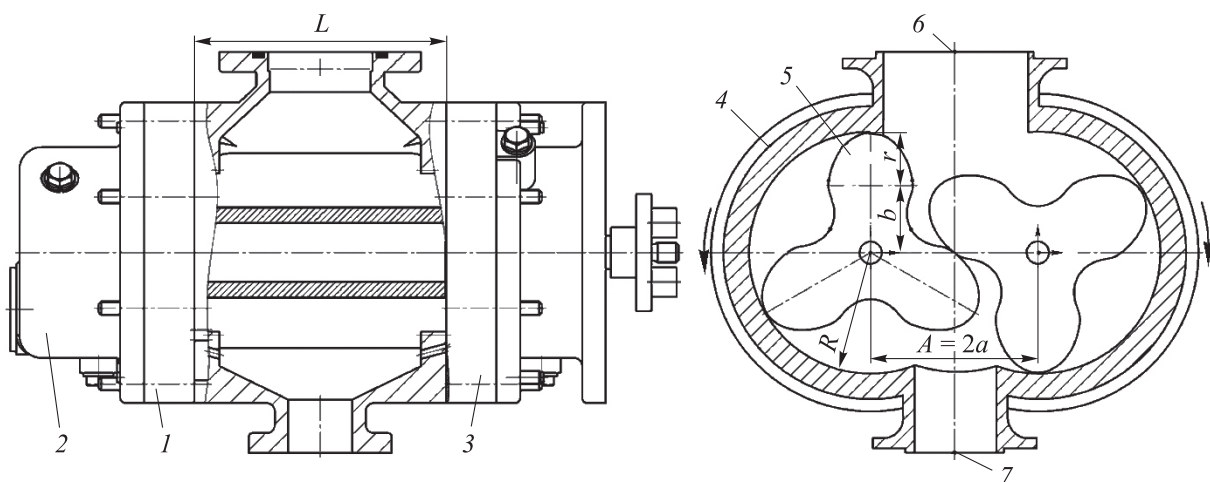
Конструктивная схема опытного образца ДВН с трехлепестковым профилем роторов: 1, 3 — торцевые крышки; 2 — масляный картер; 4 — корпус; 5 — ротор; 6 и 7 — входной и выходной патрубки
